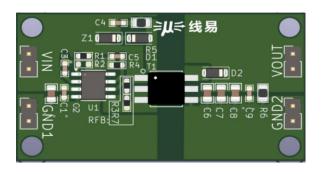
PCB 示意图 (尺寸: 25x 45mm)
